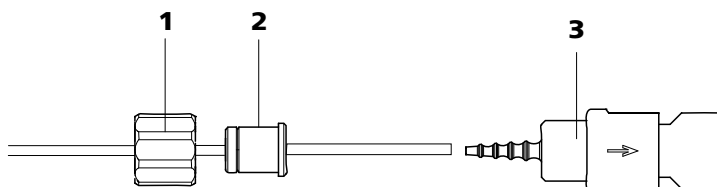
Instalar a conexão do tubo de bomba com filtro
